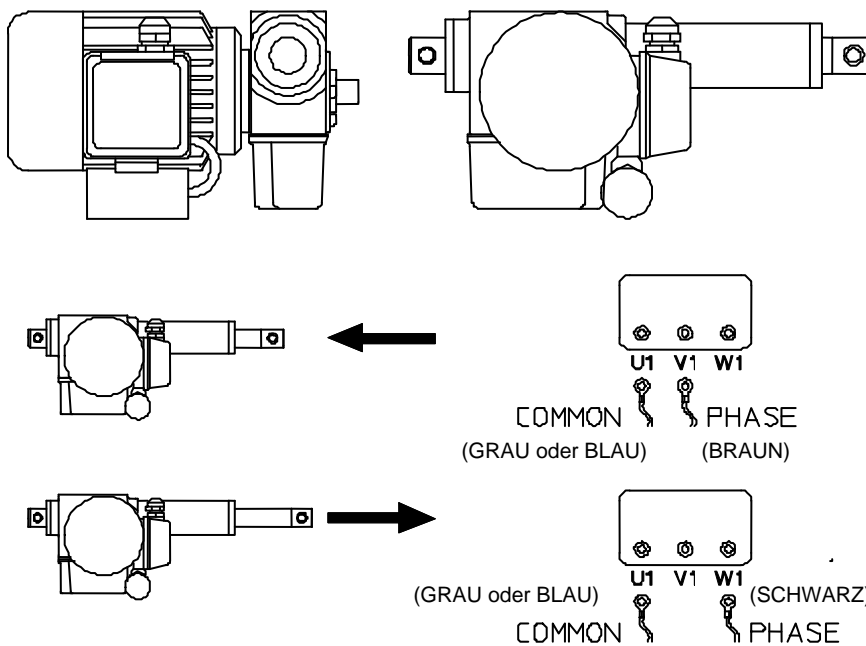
Laufrichtung mit Wechselstrommotor (1. RH und 2. LH Ausführung)
